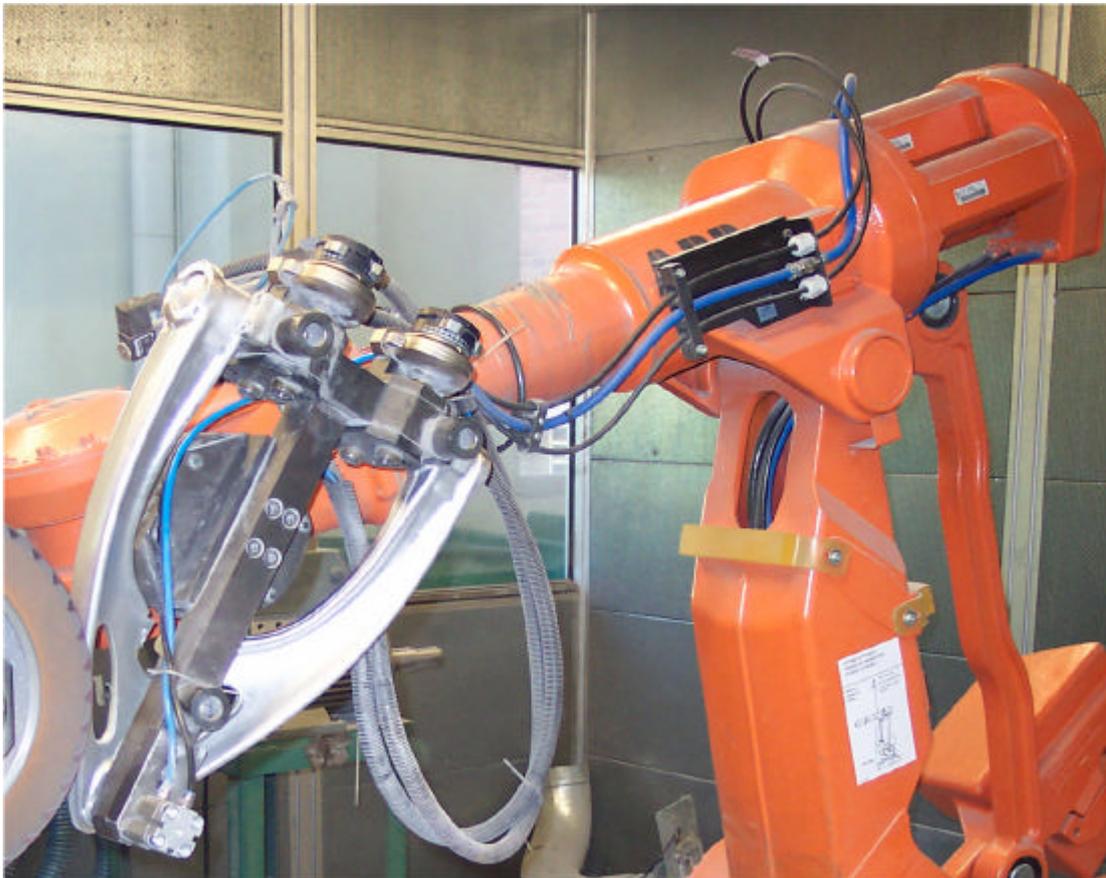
Bauteilbearbeitung Roboterschleifen
